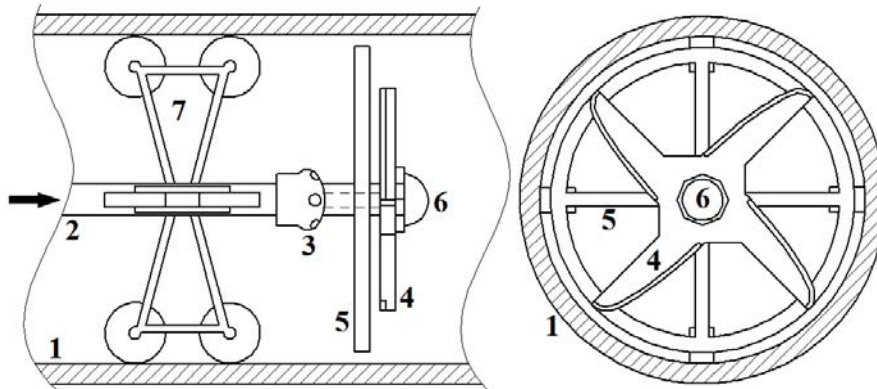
Общий вид конструкция рубящего устройства для чистки ливневых стоков
